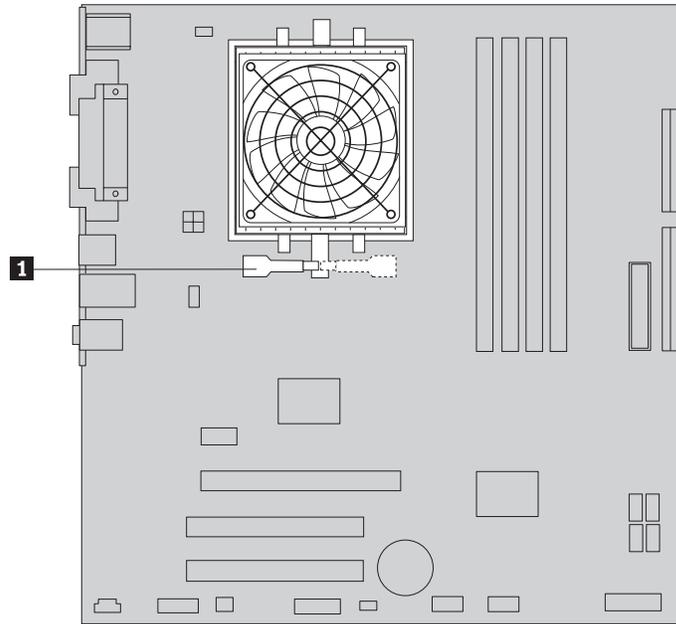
Mit einer Klemme befestigten Kühlkörper entfernen
